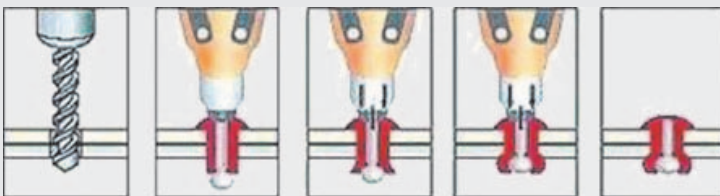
Схема прийомів з'єднання деталей витяжною заклепкою
